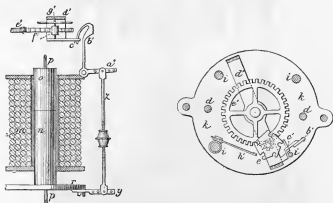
et 68. — Lampe Cance : détail de l'échappement (élévation et plan).
